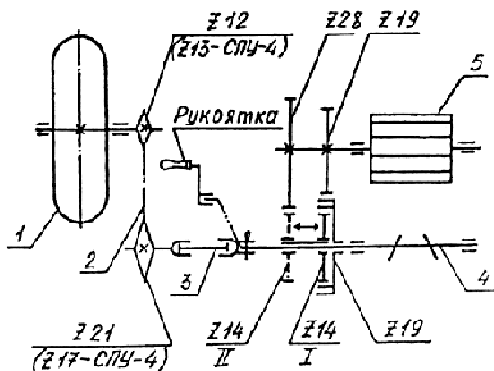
Кинематическая схема привода высевающего аппарата:
